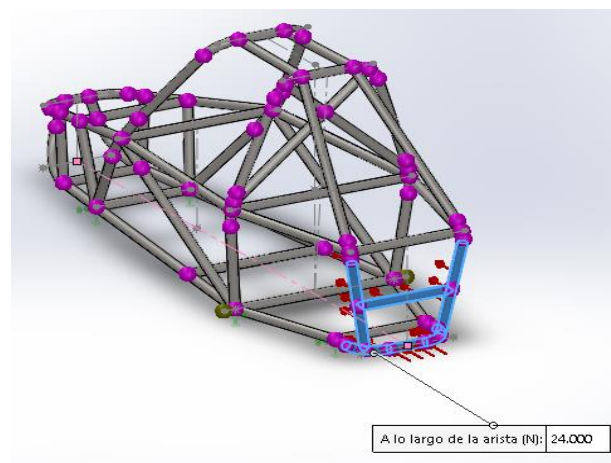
/Zona de aplicación carga longitudinal posterior.
